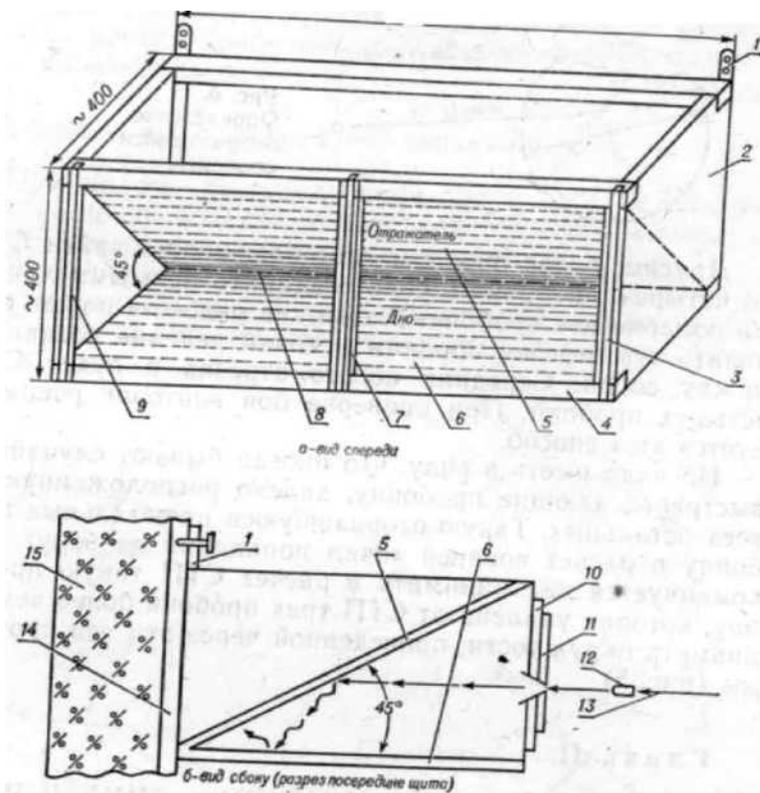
Двухщитовой пулеулавливатель для стрельбы из пневматических винтовок:
